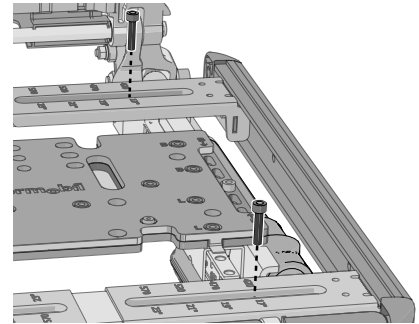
Die beiden Sitzplattenhalterungen sind mit zwei Schrauben befestigt.
